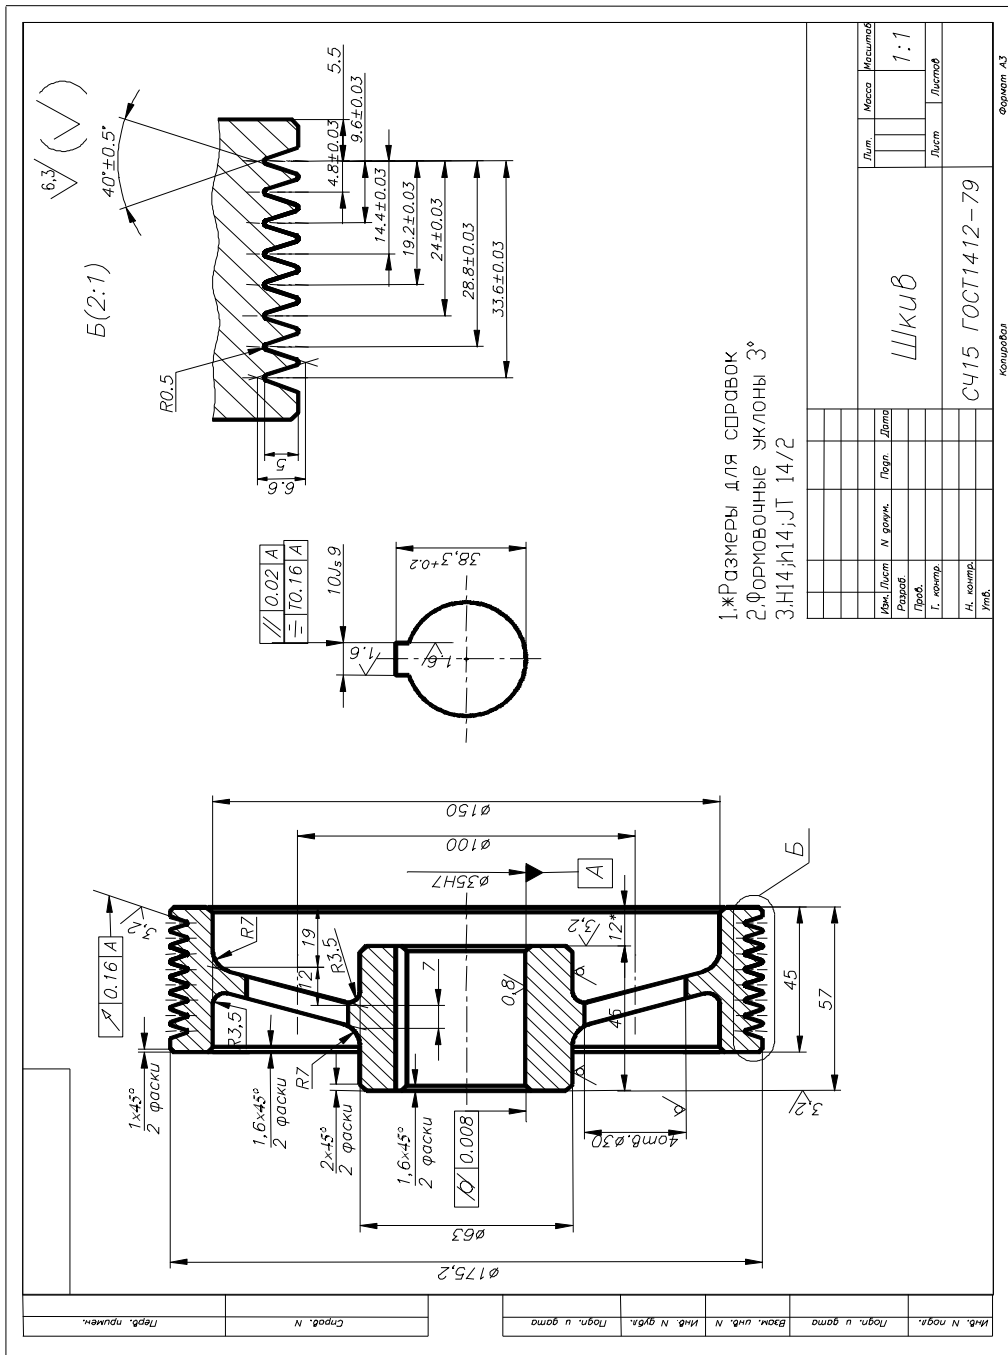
Рабочий чертеж шкива полуклиноременной передачи
